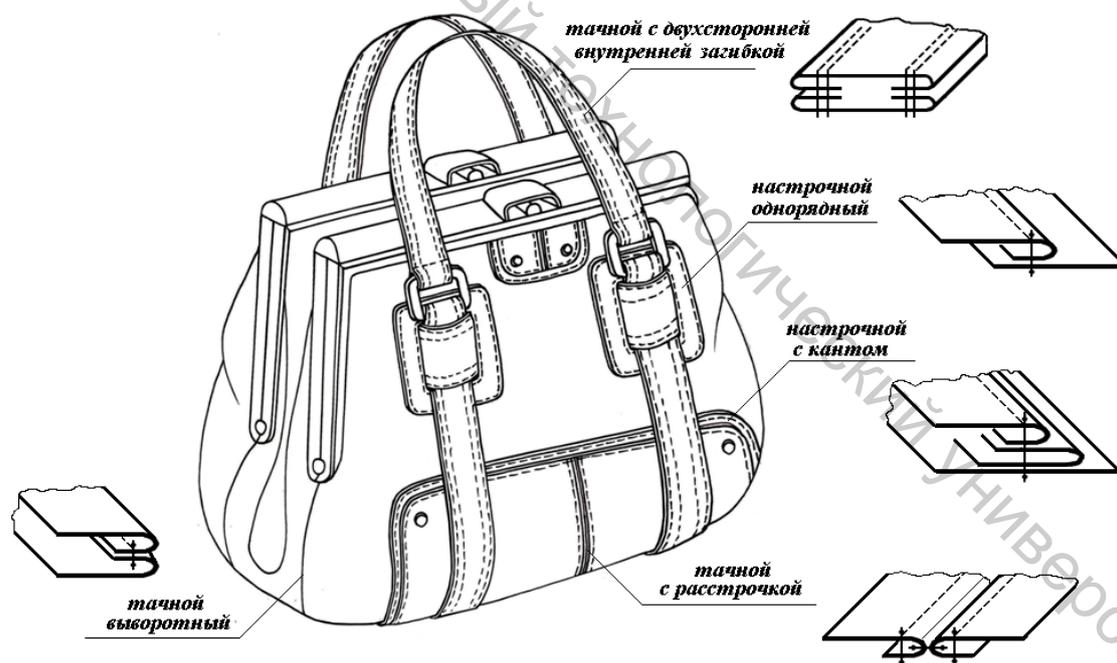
Виды и схемы соединения и обработки деталей изделия
